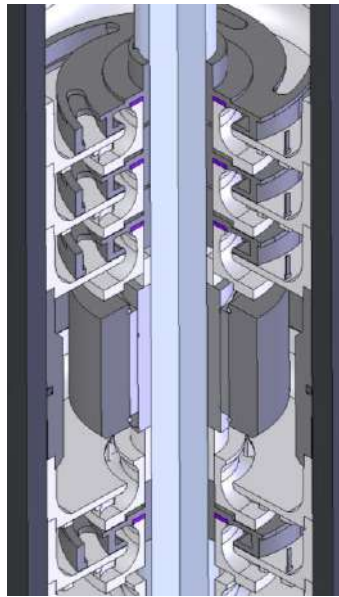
Конструкція ЕВН із відкритими робочими колесами
